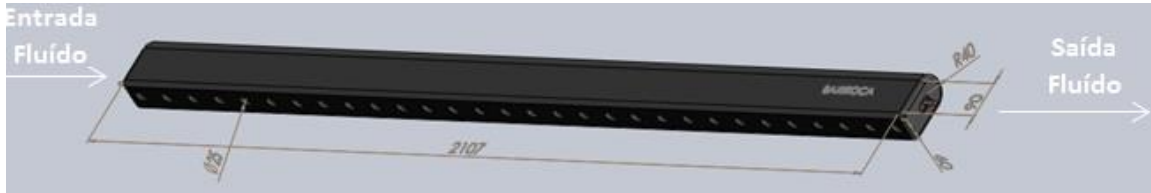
Desenho tridimensional do adaptador do coletor.
